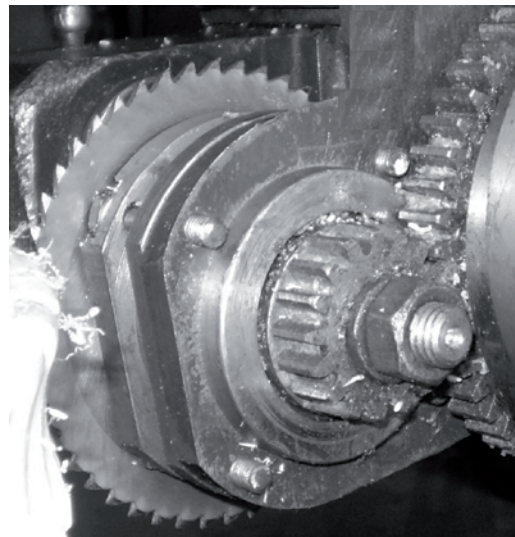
Одноступеневий мультиплікатор зубофрезерного верстату з швидкохідною дисковою фрезою
